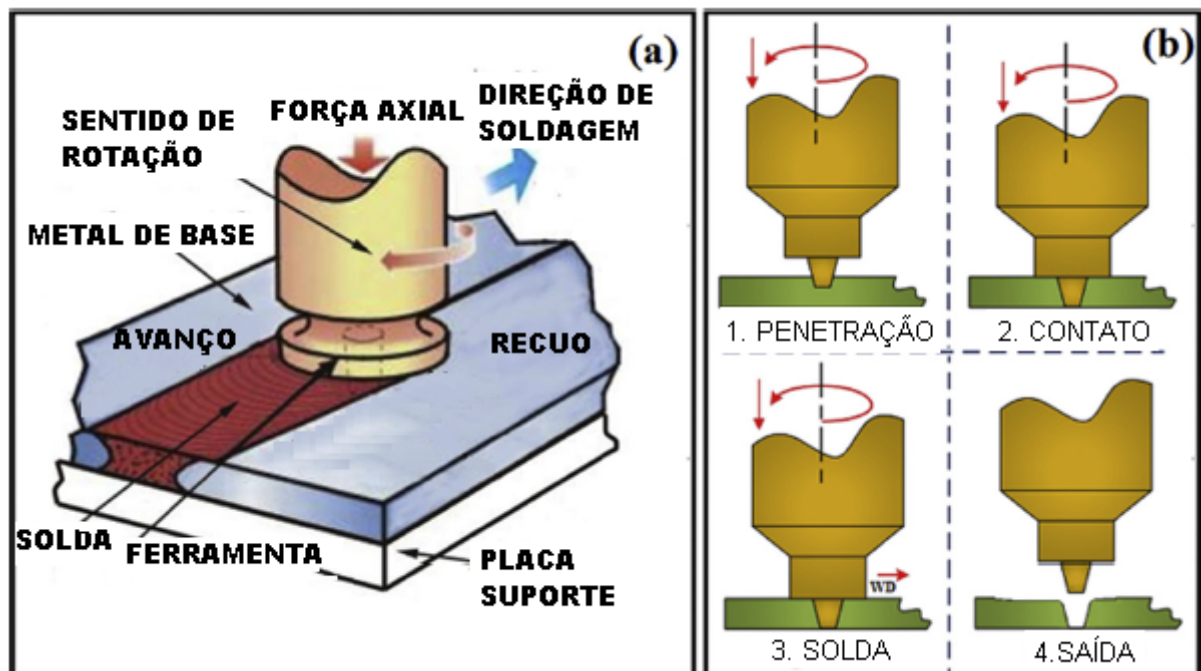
(a) Esquema de soldagem pelo processo FSW e (b) etapas em que ocorrem o processo de soldagem, adaptado [3].
